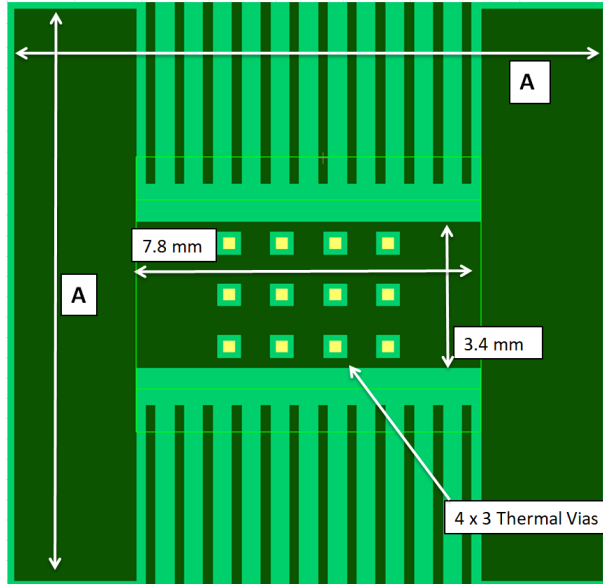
适用于 HTSSOP 封装的 PCB - 顶层 (4/2 层 PCB)
